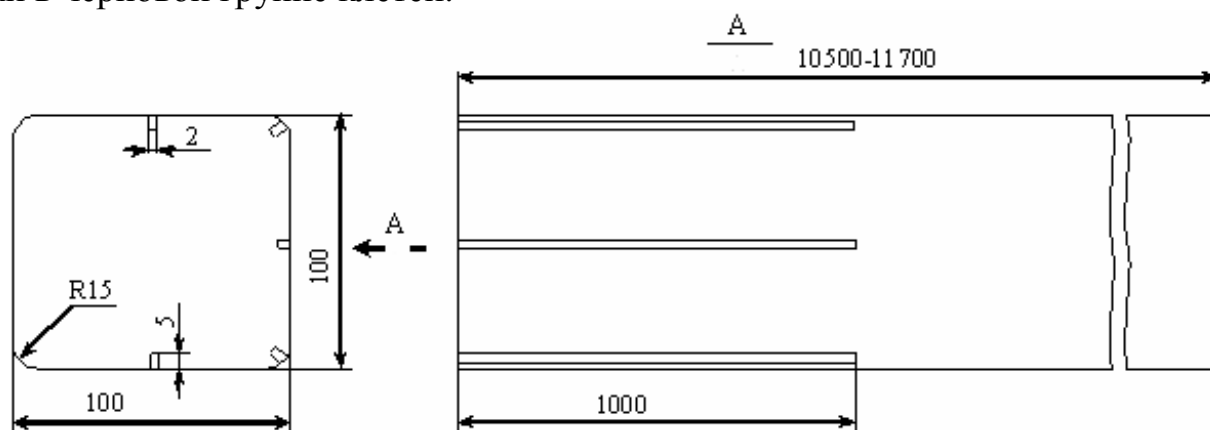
Схема нанесения искусственных дефектов на заготовки
